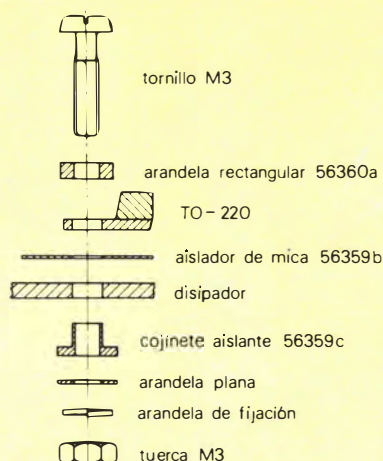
Montaje con tornillo aislado usando una arandela rectangular, (no se recomienda cuando la carcasa de montaje está sobre la fuente de alimentación). Este montaje se conoce también como «montaje inferior».
